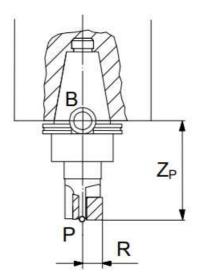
Расположение точки установки инструмента на фрезерном станке
